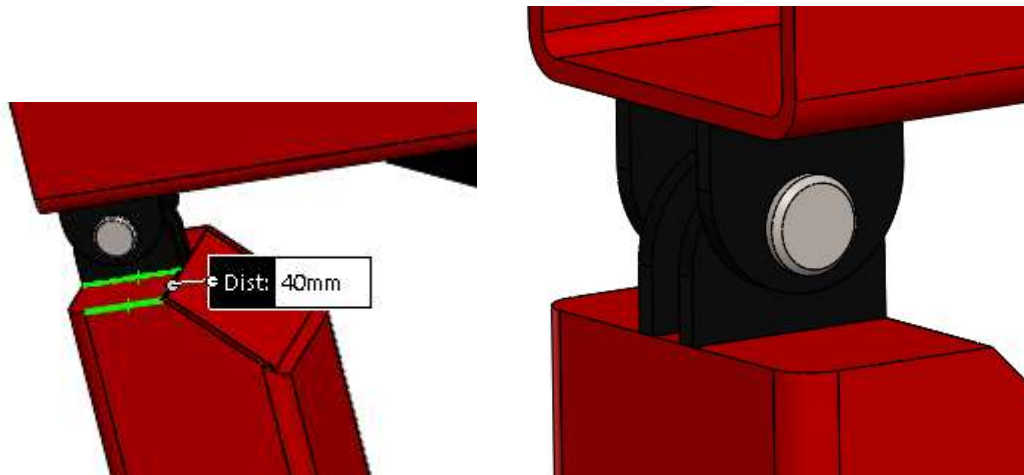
Disposición lateral de las placas de unión pluma-pilar.
